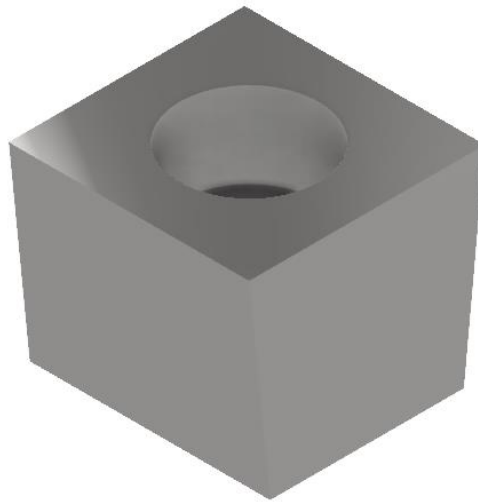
Зовнішній вигляд клину тристоронньої фрези дискової збірної
